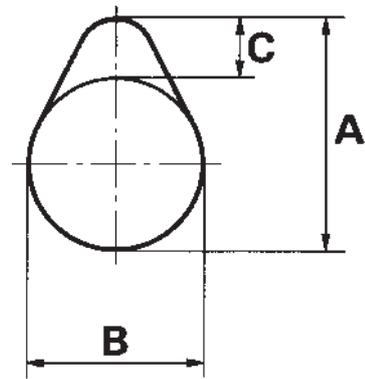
C. Mesure du levage d'arbre à cames C (hauteur de cames)
